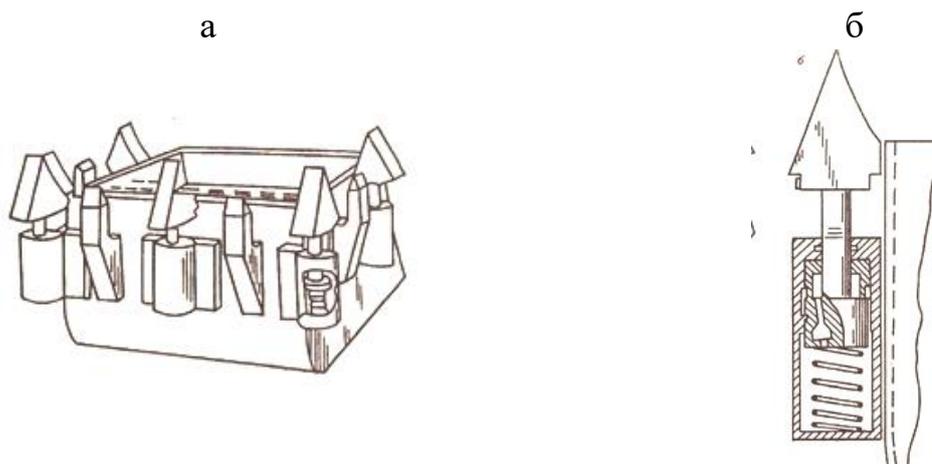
Ковш роторного экскаватора с виброзубьями (патенту № 3550960 США) а – общий вид, б – виброзуб
